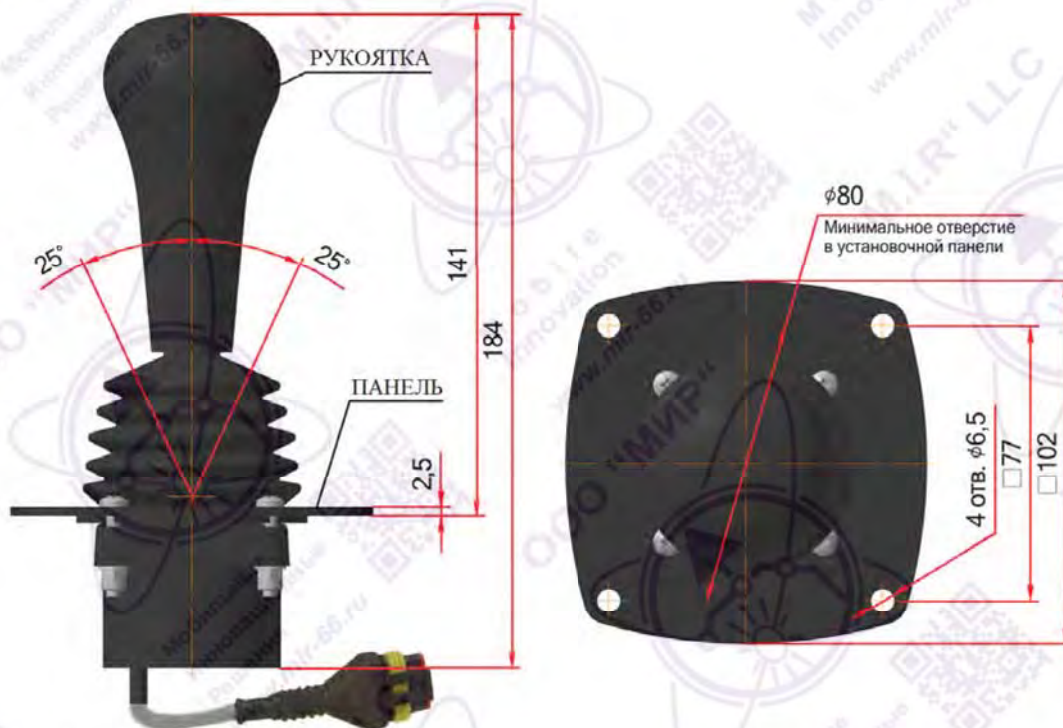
Внешний вид и габаритно-присоединительные размеры джойстика с переходной пластиной.
